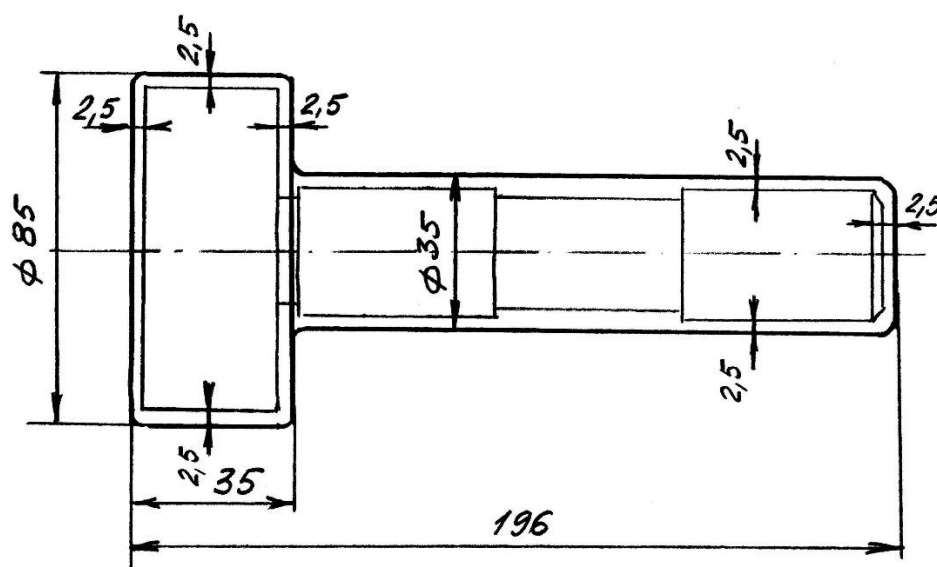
заготовка – поковка, штампованная на ГКМ
